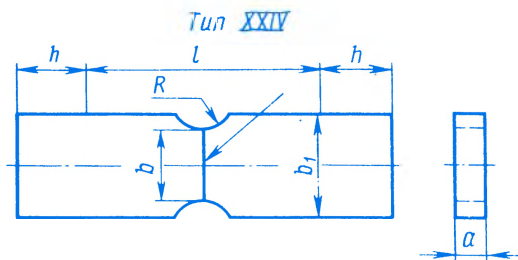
Образец для определения прочности металла шва в стыковом соединении:
